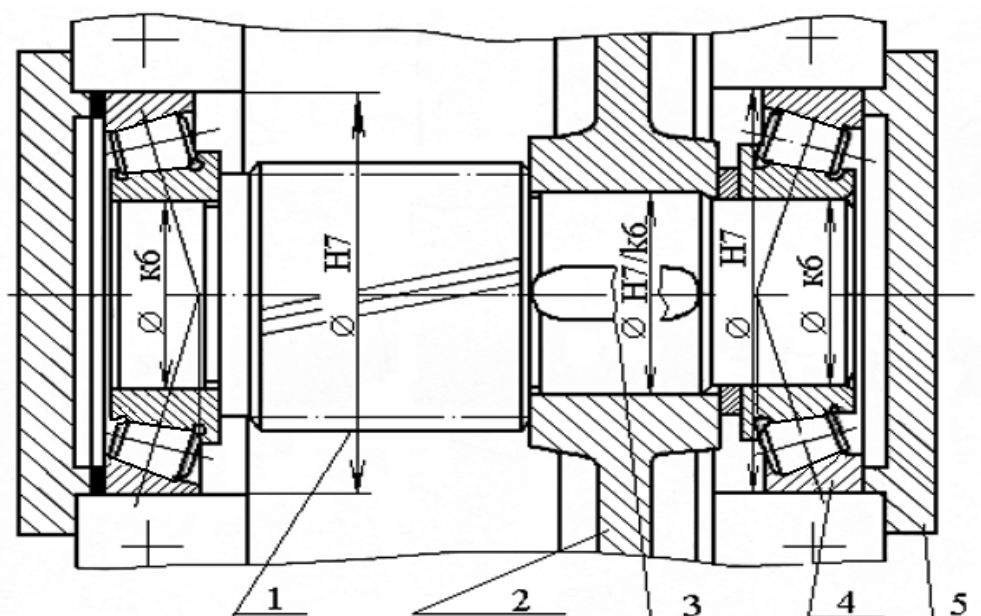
Вал с опорами: 1 – вал-шестерня; 2 – колесо; 3 – шпонка; 4 – подшипник; 5 – крышка подшипника
